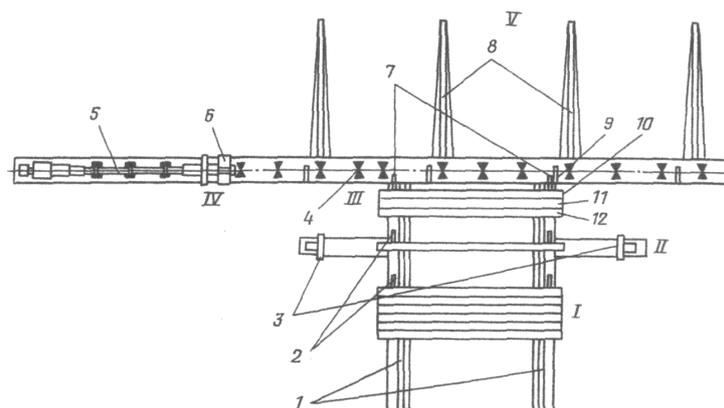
Схема установки типа ПЛТ для электроконтактной сварки труб:
